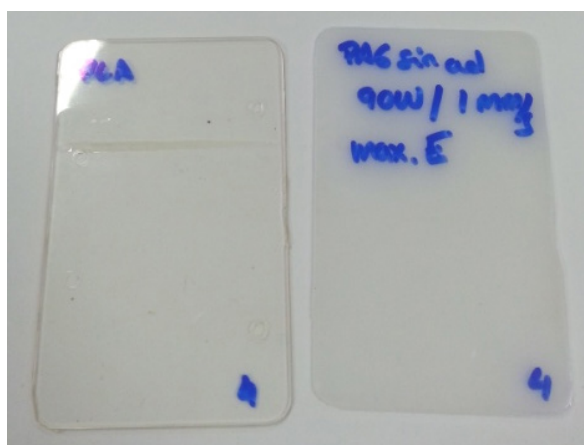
Resultado de soldadura láser entre PA6 pura y PLA.
